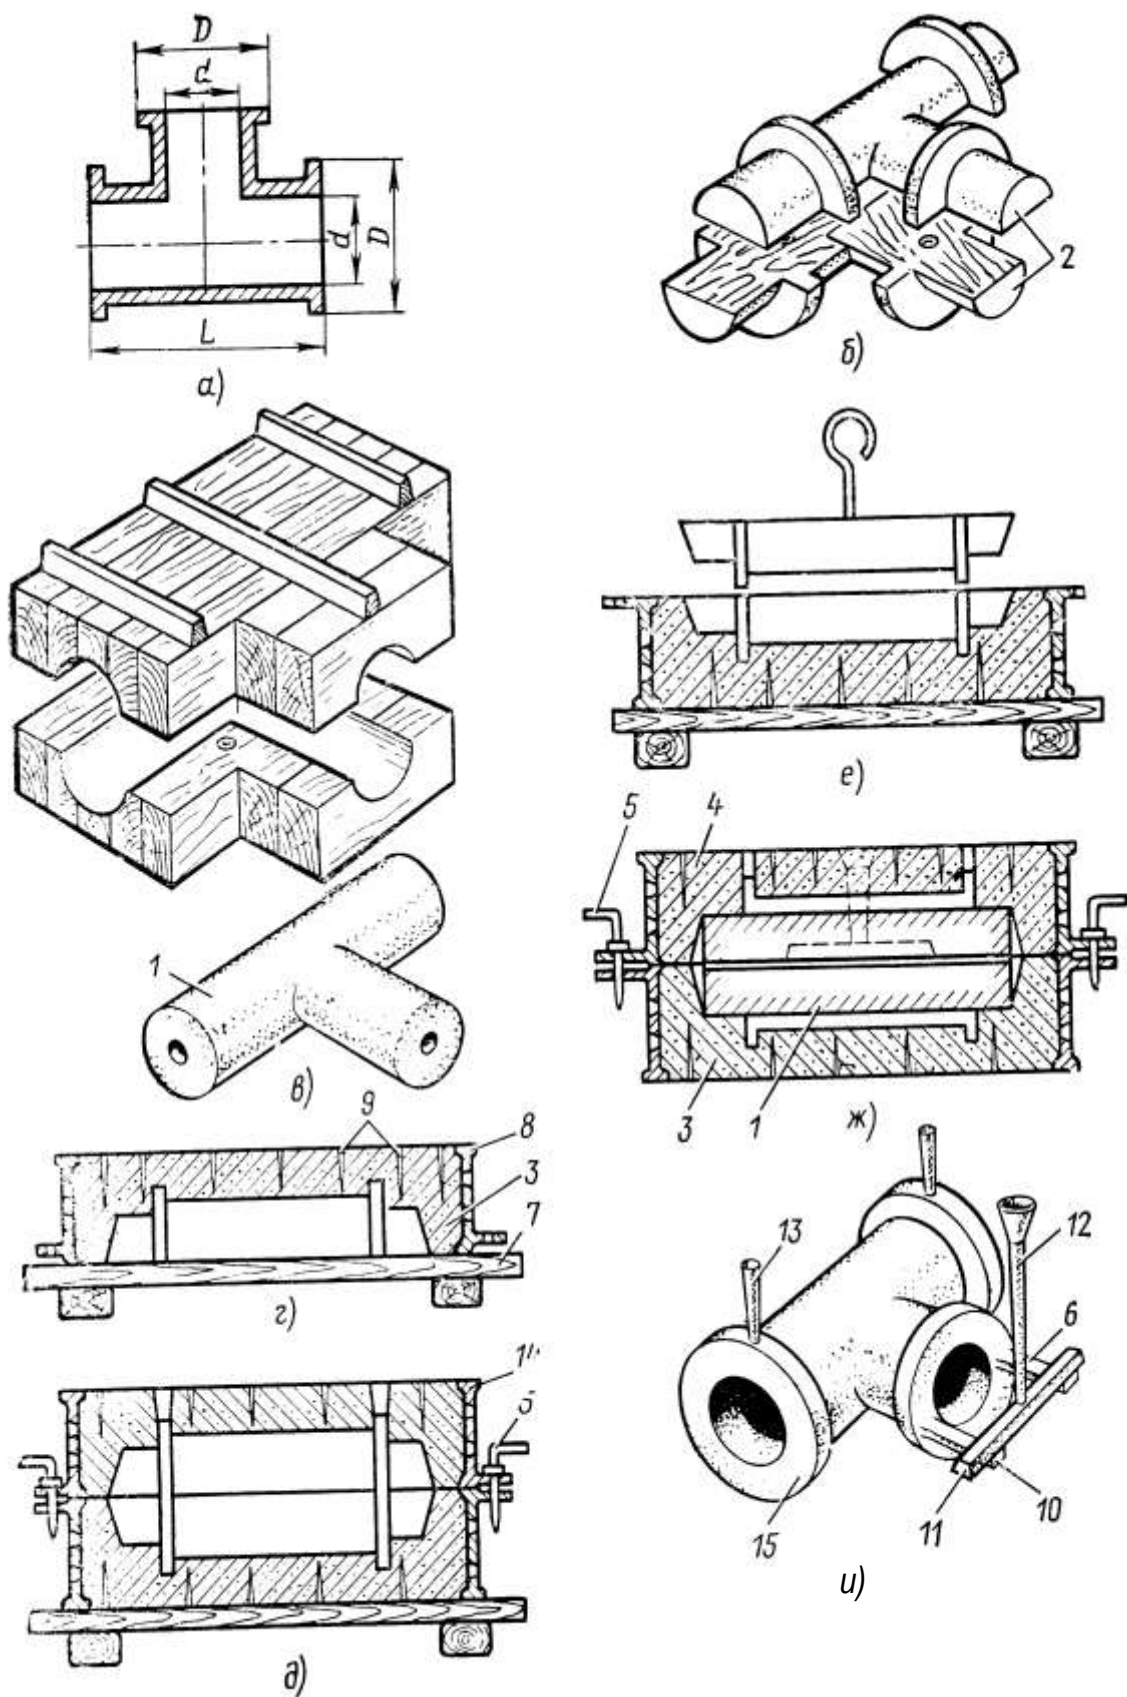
Послідовність виготовлення ливарної форми у двох опоках за роз'ємною моделлю
